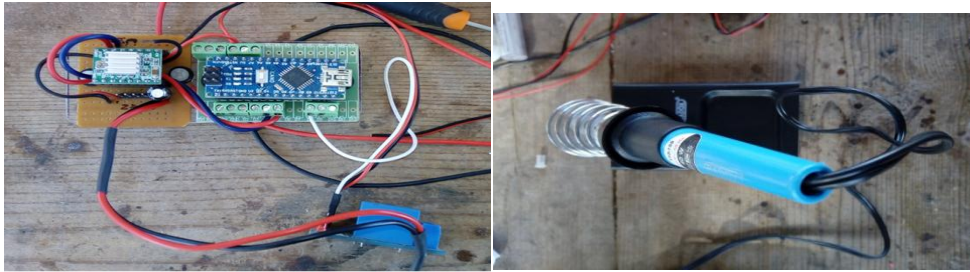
Conexiones del circuito controlador del brazo robot y cautin para soldar
